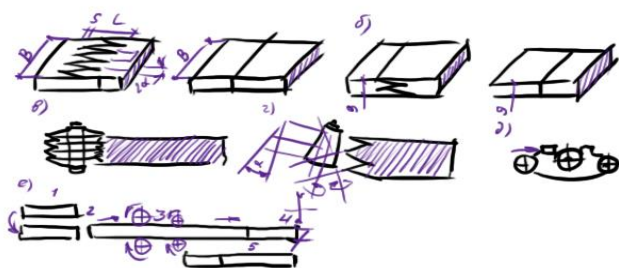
Торцевые наращивания схемы фрезерования при торцевом склеивании заготовок:
